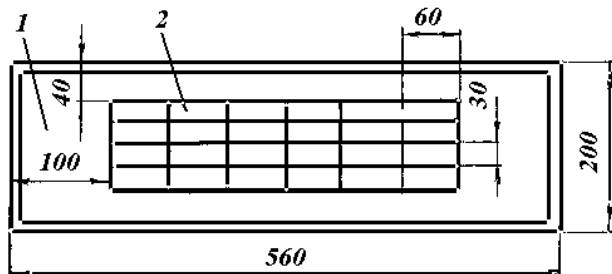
Схема расположения заготовок на магнитной плите плоскошлифовального станка:
